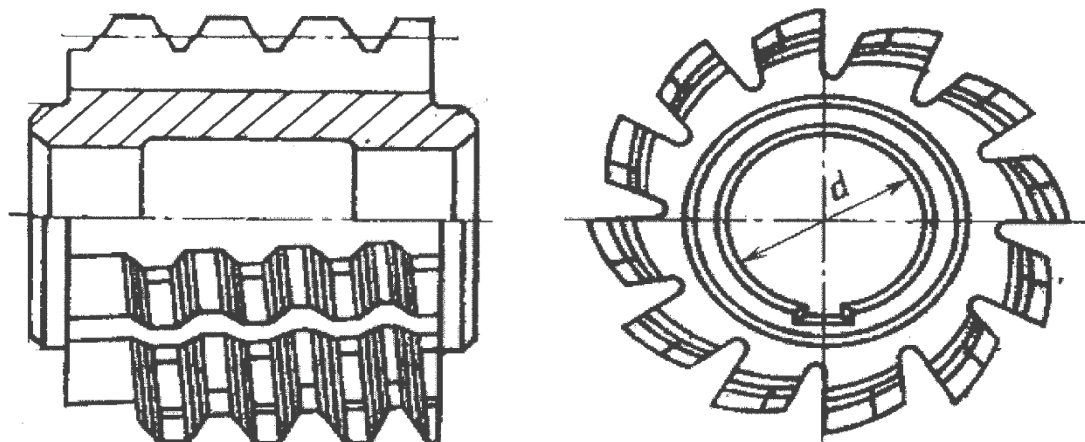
Фреза червячная для шлицевых валов с прямобочным профилем. ГОСТ 8027-86
